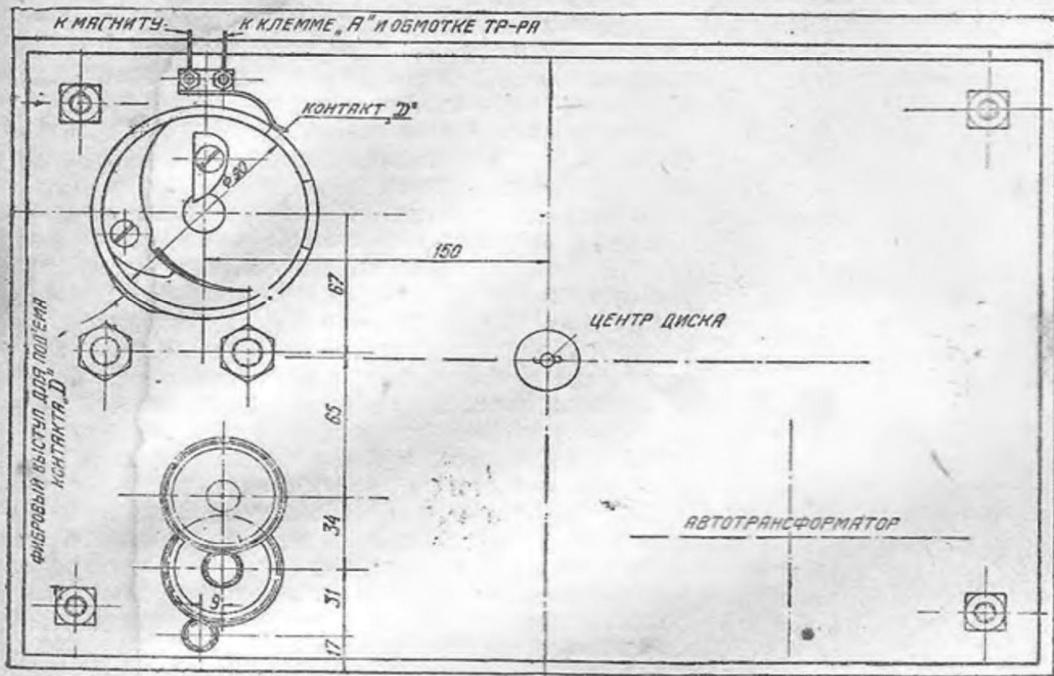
Нижняя доска автомата (вид сверху). Показано расположение перевода и шестеренчатого перебора. У перевода виден контакт блокировки магнитного пускателя и размыкающая его пластина
